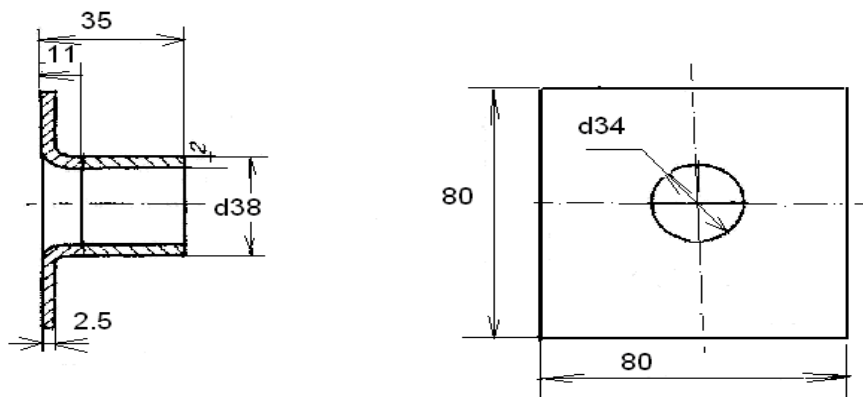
Зразки для досліджень стикового зварного з'єднання труби з тонкими решітками.
